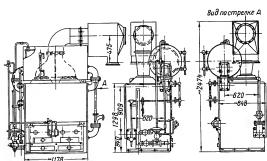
Габаритные размеры парового котла "ЛУЧ" с поверхностью нагрева 14,72 м²
